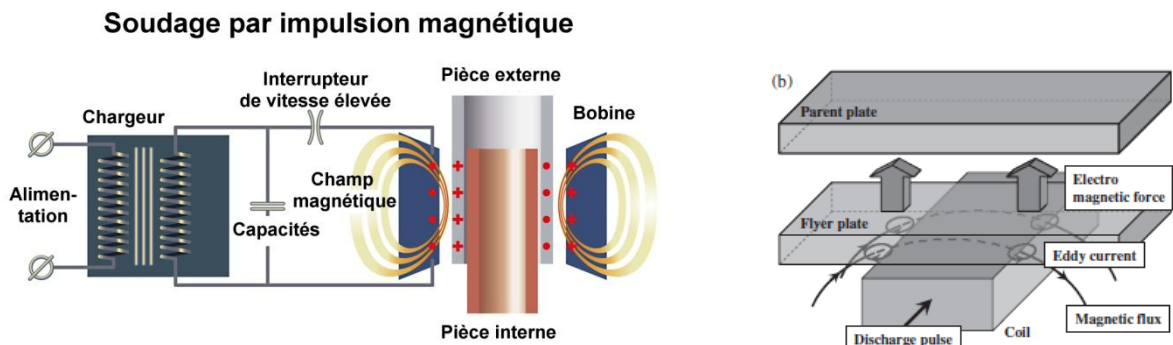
Assemblage magnétique (a) : compression de tubes [23]. (b) : assemblage de plaques [24]
